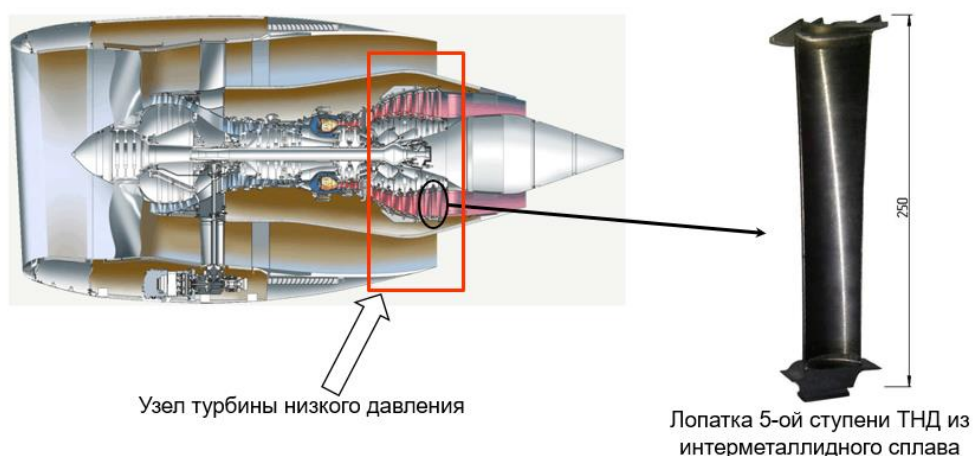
Схема двигателя ПД-14 и фотография лопатки из сплава TNM-B1
